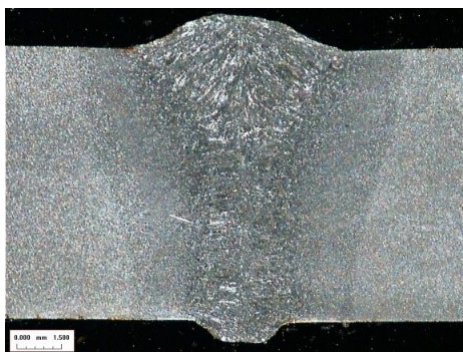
Макрошлиф сварного шва, полученного гибридным лазерно-дуговым способом сварки, толщина 10 мм
